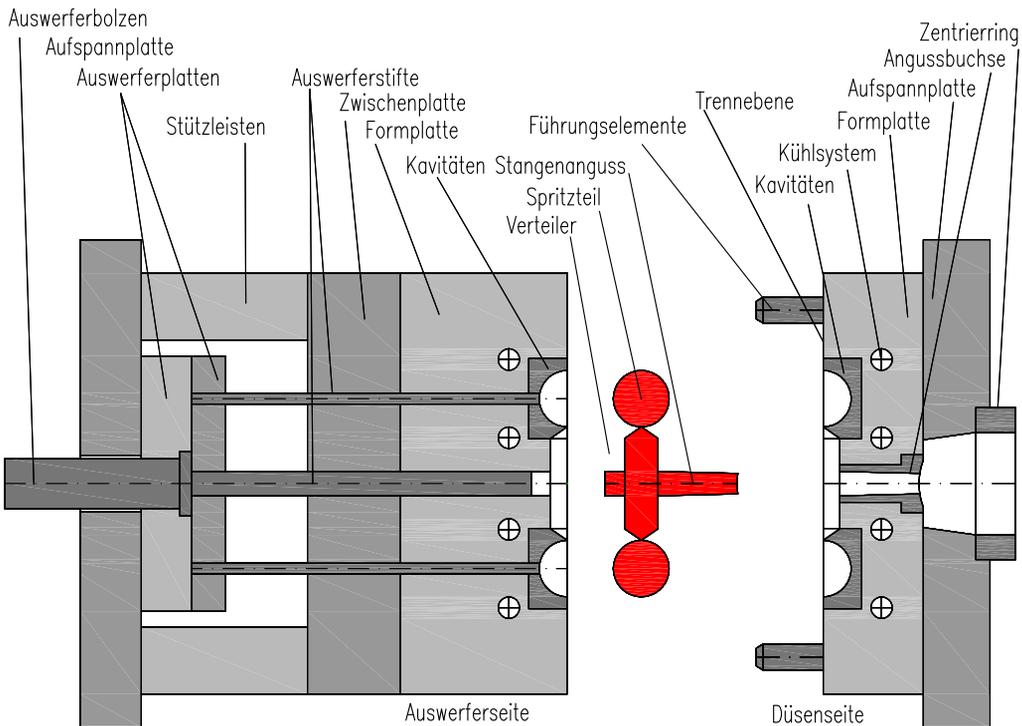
Prinzip Zweiplatten-Werkzeug
